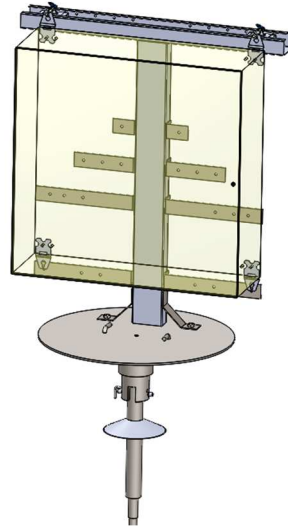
Conjunto soporte de gabinete - Mecanismo de inclinación
